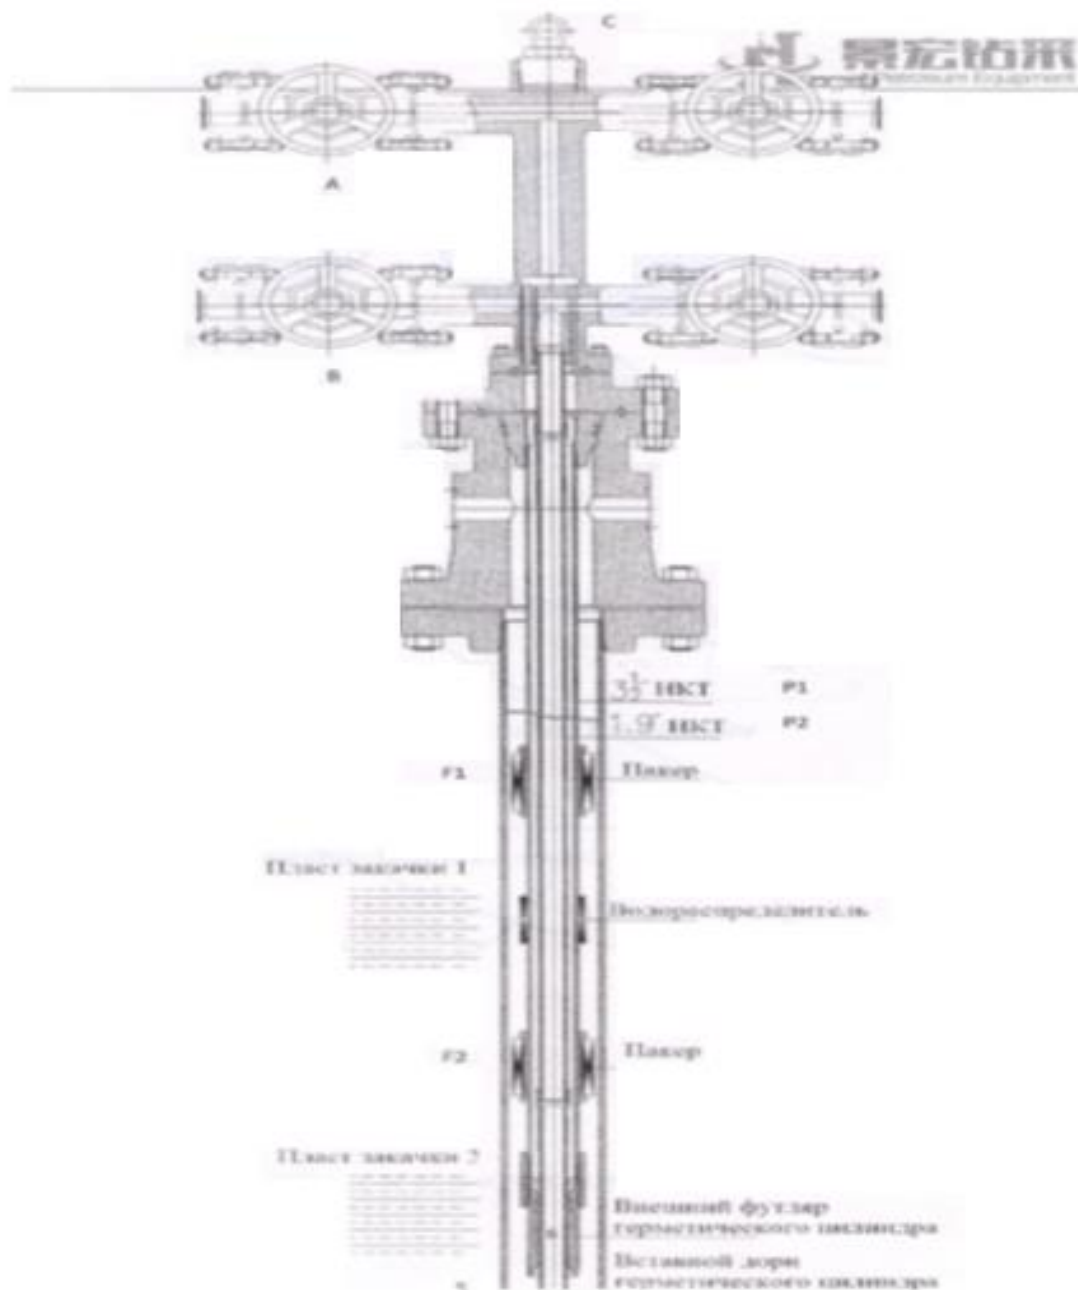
Конструкция двухтрубного оборудования ОРЭ
